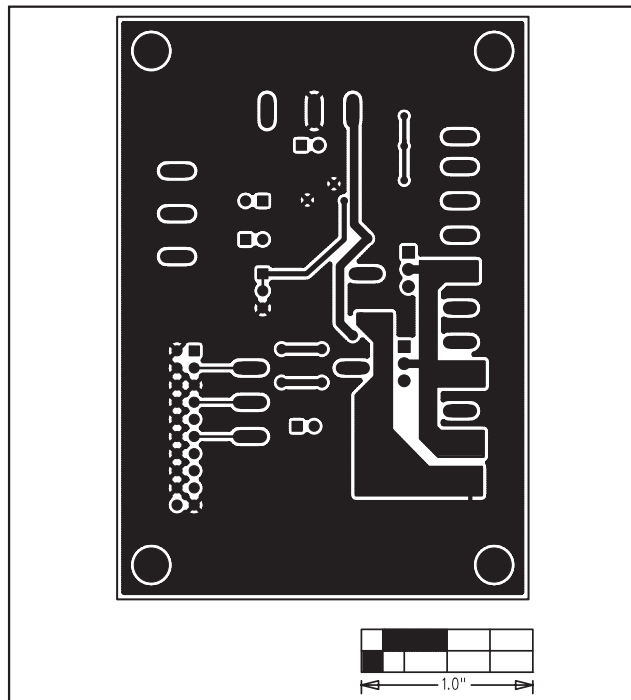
MAX6640 评估板PCB 布局—焊接层
